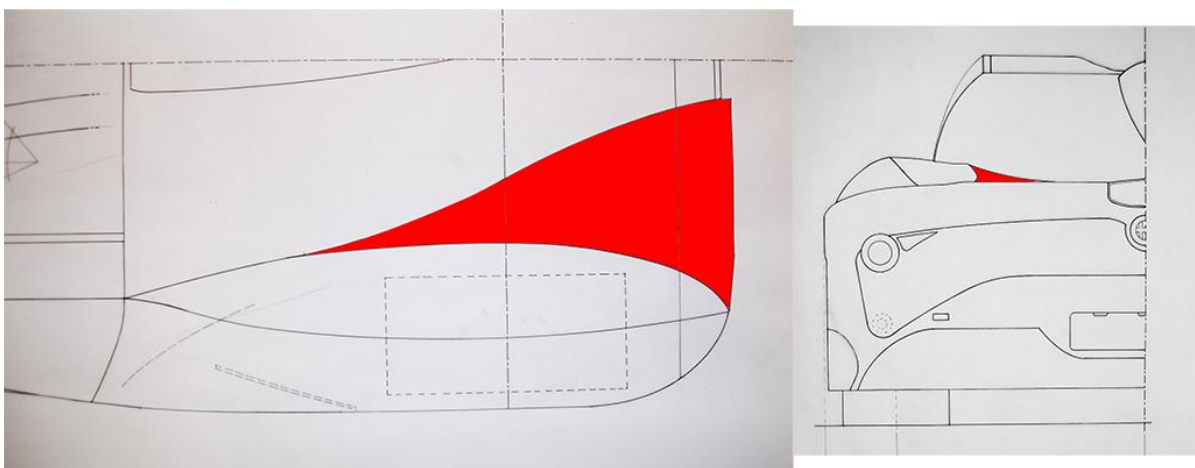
in rosso la superficie appena illustrata, vista in pianta e sul prospetto posteriore
